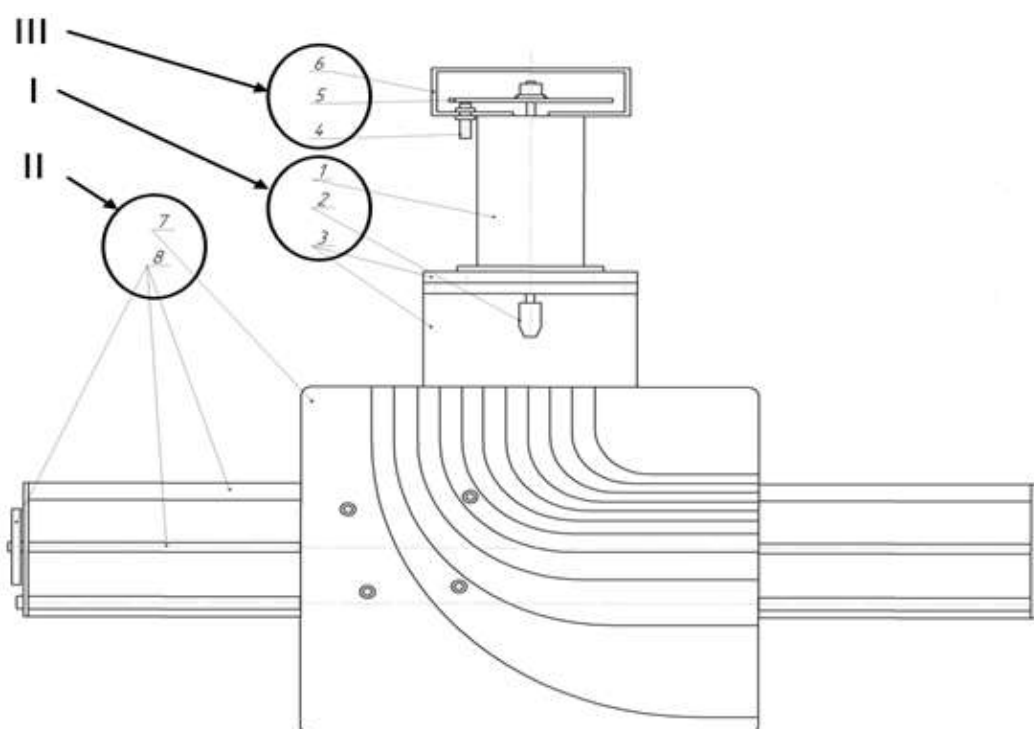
Схема спроектированной установки для усталостных испытаний проволоки:
